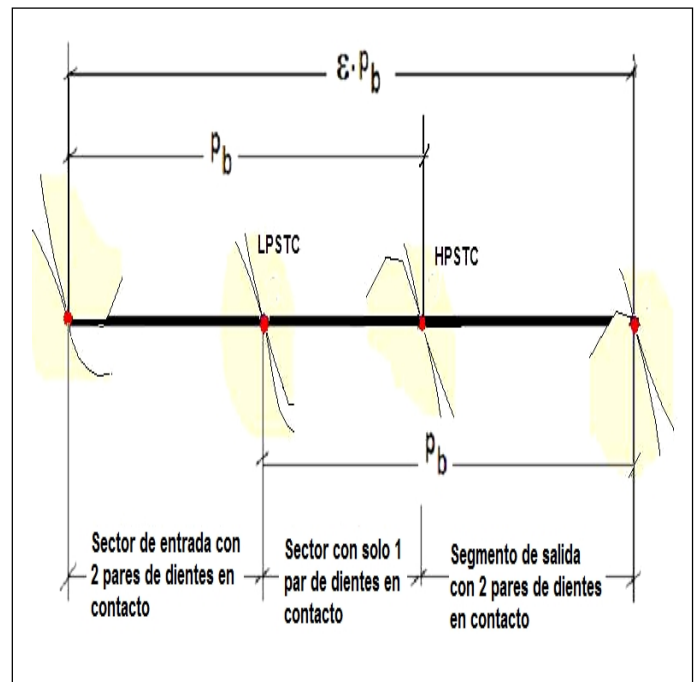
Diferentes sectores del engranaje con 1 y 2 pares de dientes en contacto sobre la línea de engranaje ($1 \leq \epsilon_\alpha \leq 2$)
